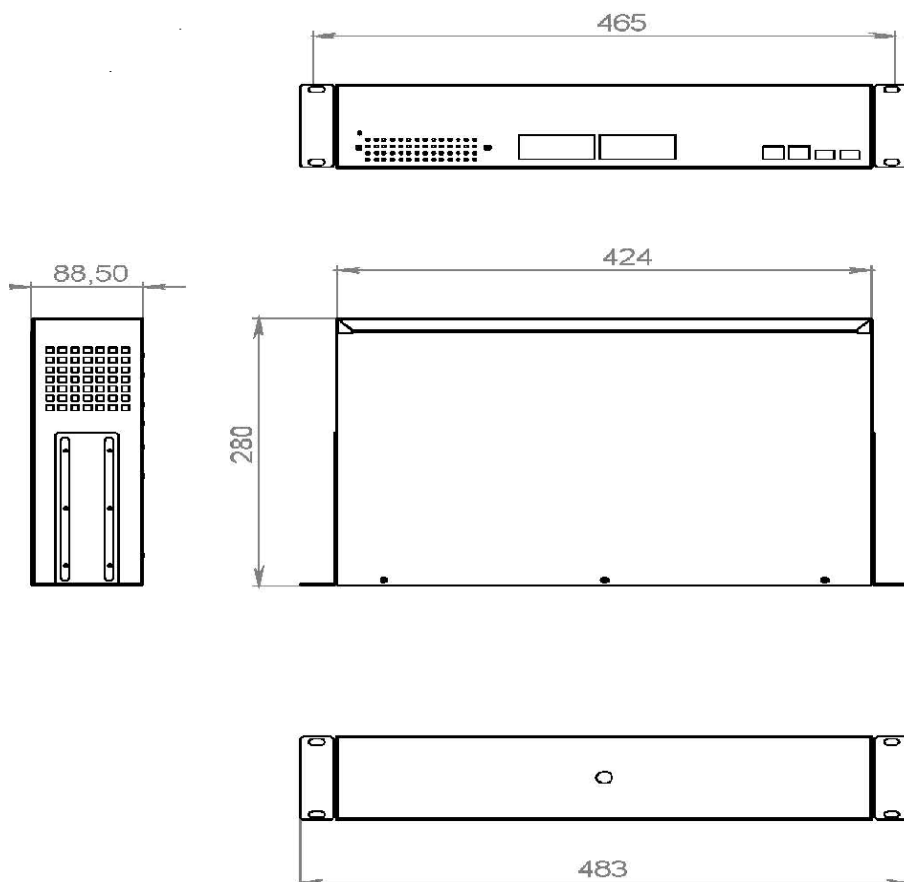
Габаритный чертеж коммутатора ИВК-16.
